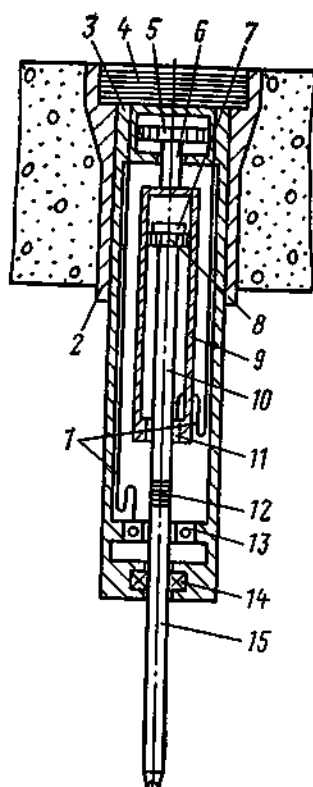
Пневматический исполнительный механизм СУЗ реактора ТНТР-300
